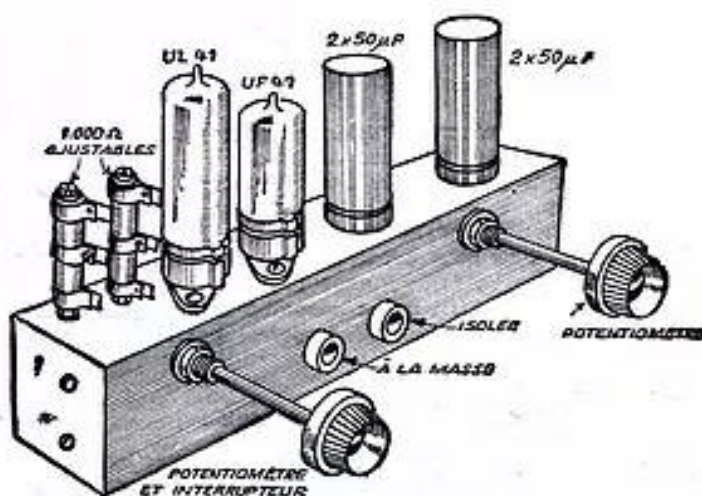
Vue d'ensemble de l'amplificateur miniature.
